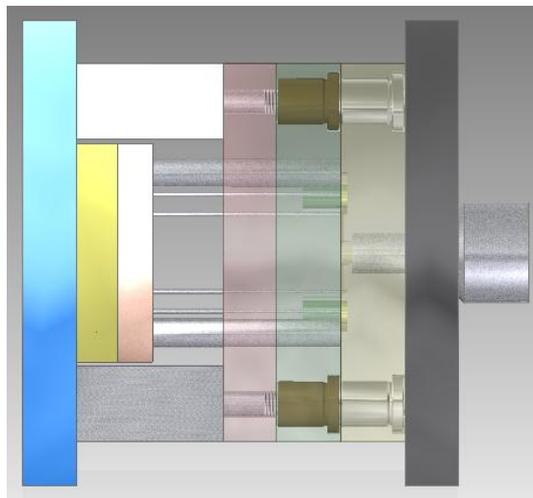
Paso 1: Molde en posición sin inyectar material
